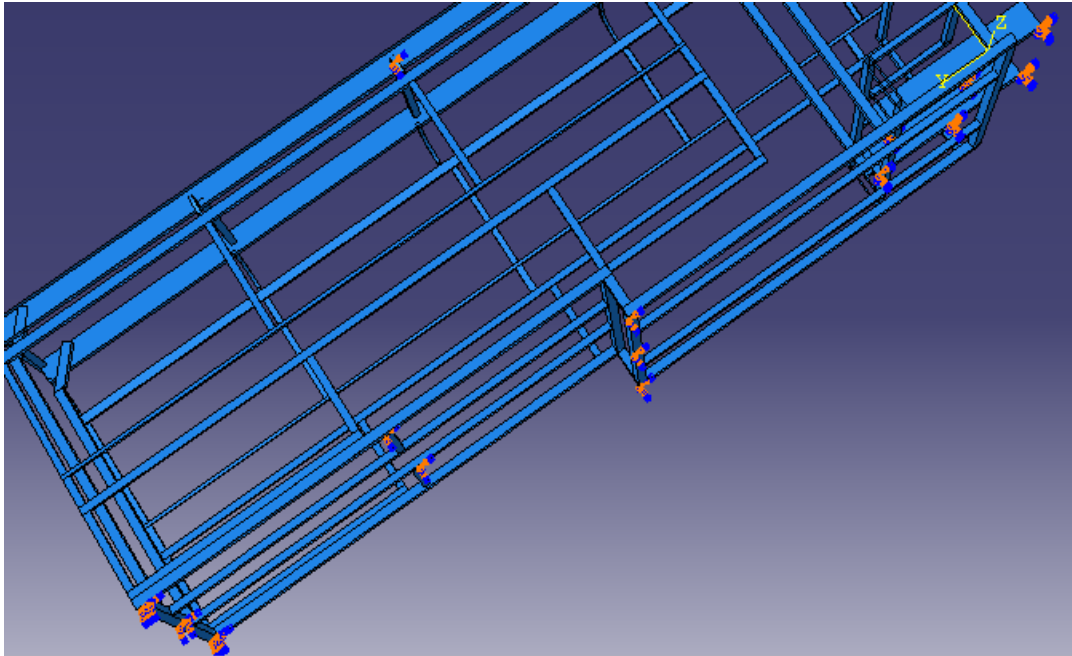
Vista de la estructura con un encastre finalizado.
